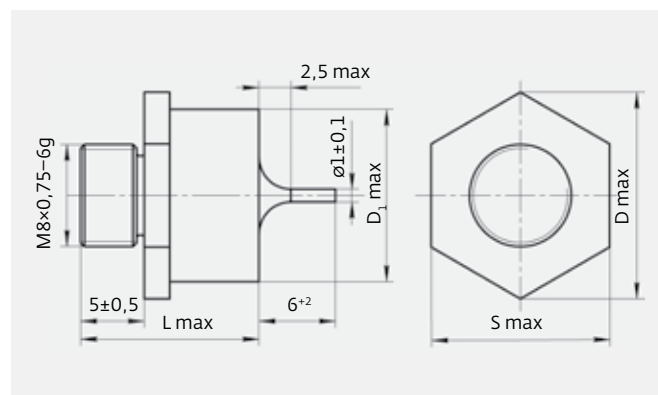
Конструкция и размеры (см. табл.1) конденсаторов с номинальным напряжением 500, 750 и 1000 В
